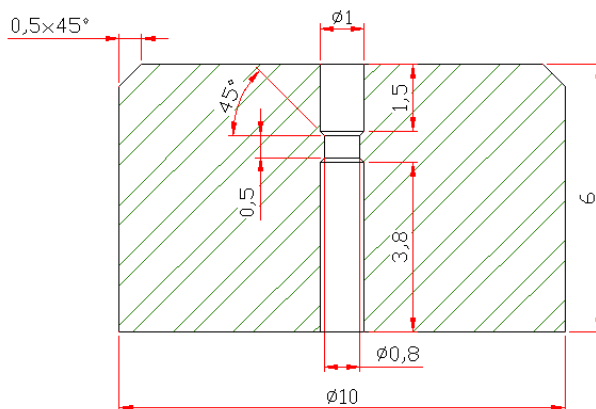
Esquema da extrusão com pino, montagem antes da extrusão.
